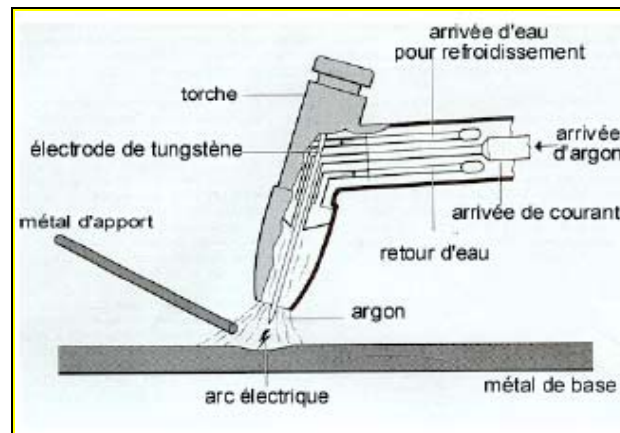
Principe du soudage par le procédé T.I.G
